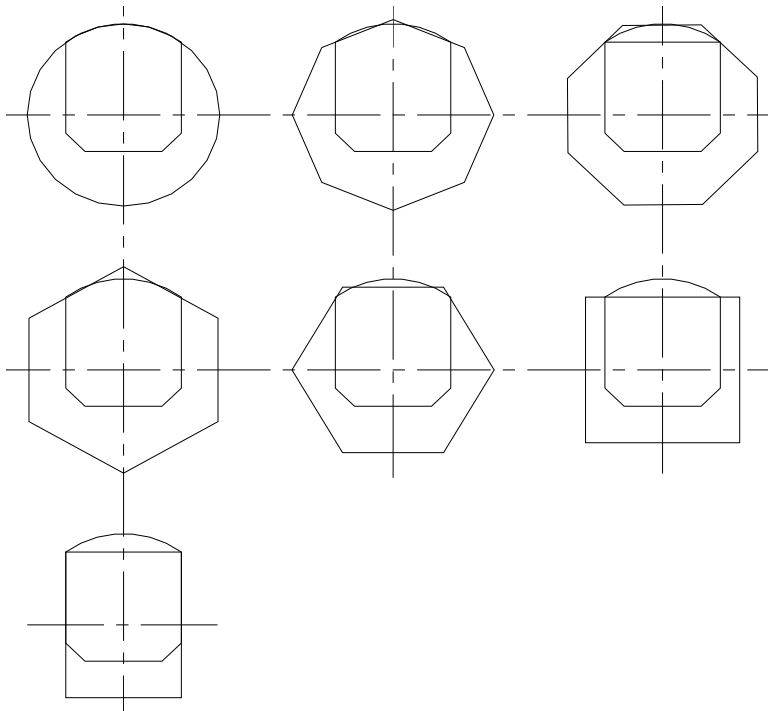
Альтернативные профили заготовок с наложенным сечением резцедержателя.
